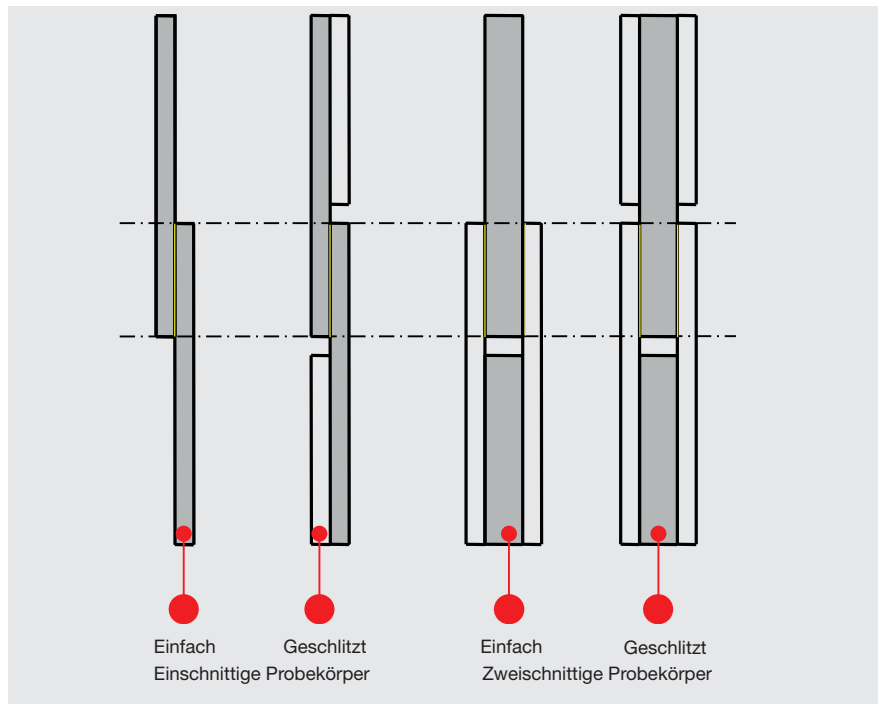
Schubversuche durch Überlappung werden mit ein- oder zweischnittigen Probekörpern, in einfacher oder geschlitzter Ausführung durchgeführt.
